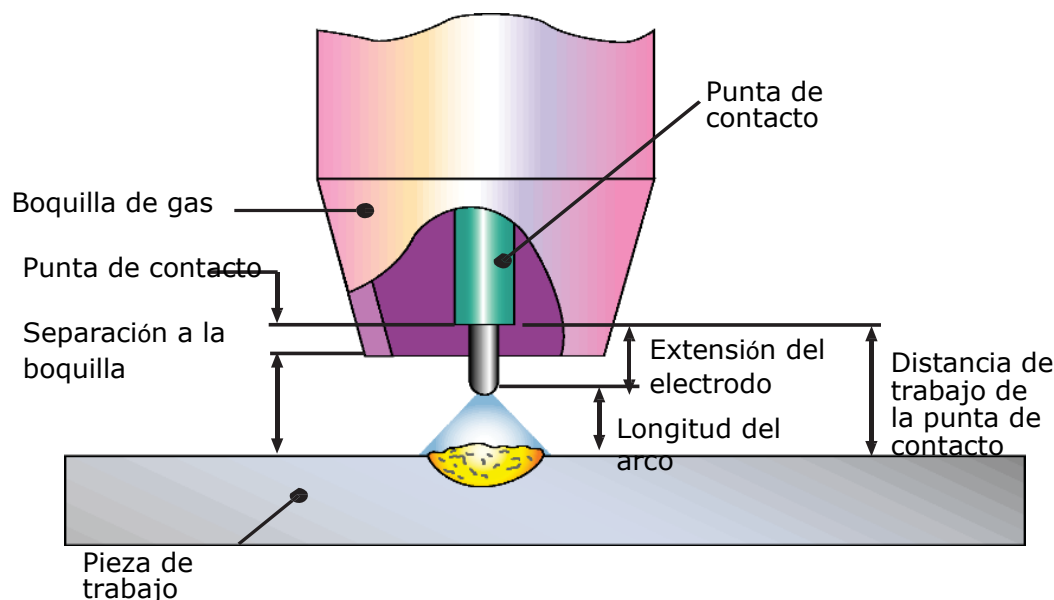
Distancia de trabajo de la punta de contacto a la pieza de trabajo; extensión del electrodo y distancia de la boquilla a la pieza de trabajo. Fuente: TWI
